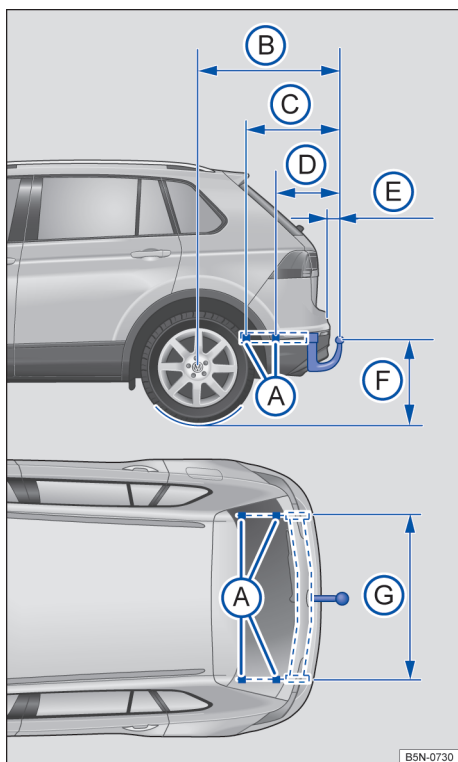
Dimensões e pontos de fixação para instalar um dispositivo de reboque posteriormente.
